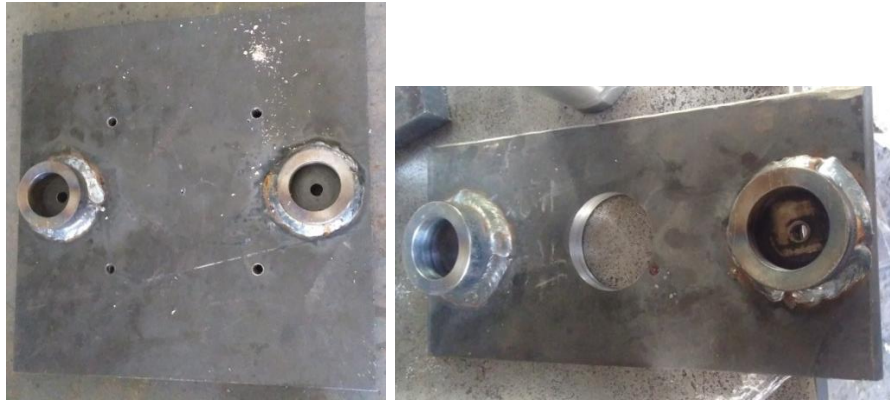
Placas superior e inferior con sus bujes soldados
